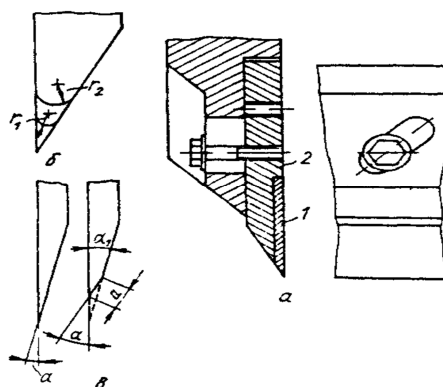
Обладнання системи різання (ножа): 1 - лезо; 2 - корпус
